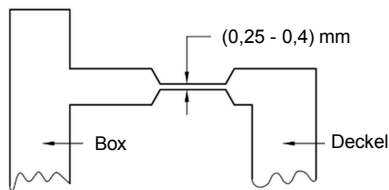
Ungünstige Ausführung einer Gelenkverbindung
